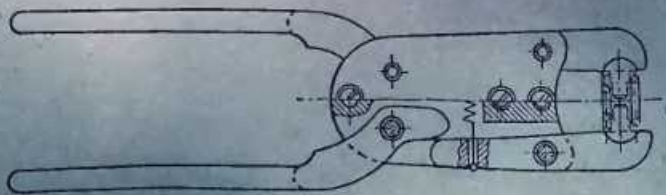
Клещи ЛМ9690-166 для установки грибков и пружин в упругую шестерню топливного насоса
